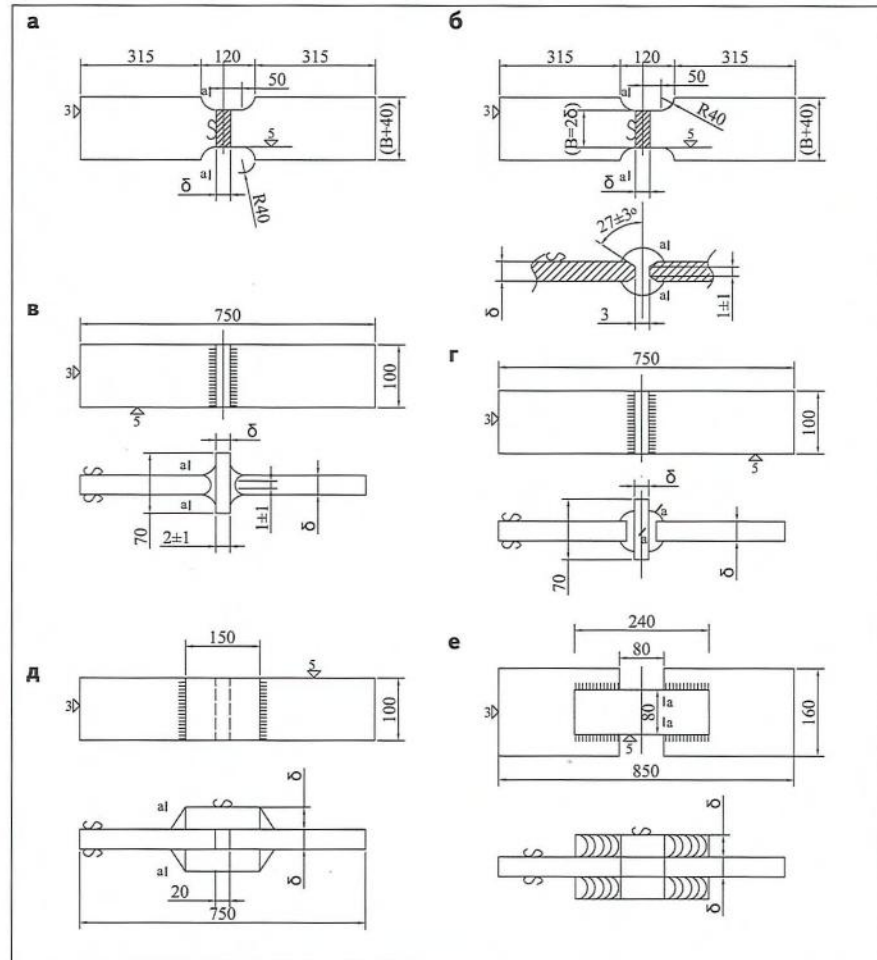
Основные типы сварных образцов для малоцикловых испытаний
